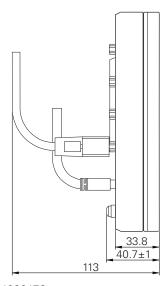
Bemaßungen des Gehäuses der Geräte mit ID 1089178-xx
